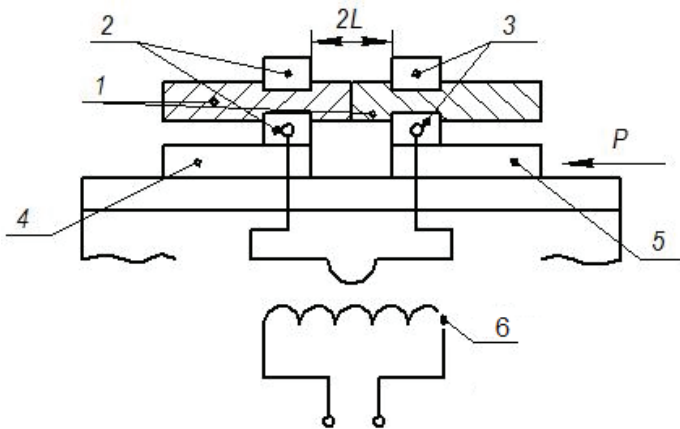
Схема контактной стыковой сварки: 1 — свариваемые заготовки; 2, 3 — зажимы; 4 — неподвижная плита; 5 — подвижная плита; 6 — сварочный трансформатор
